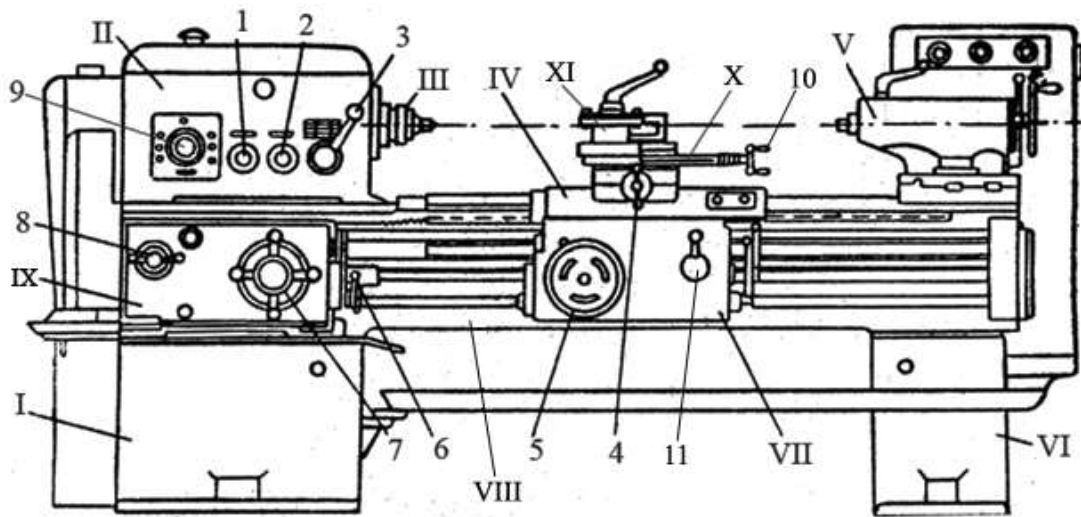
Загальний вигляд токарно-гвинторізного верстата
